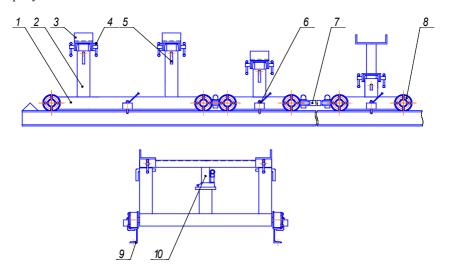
Стенд для разборки-сборки трактора МТЗ-80/82
